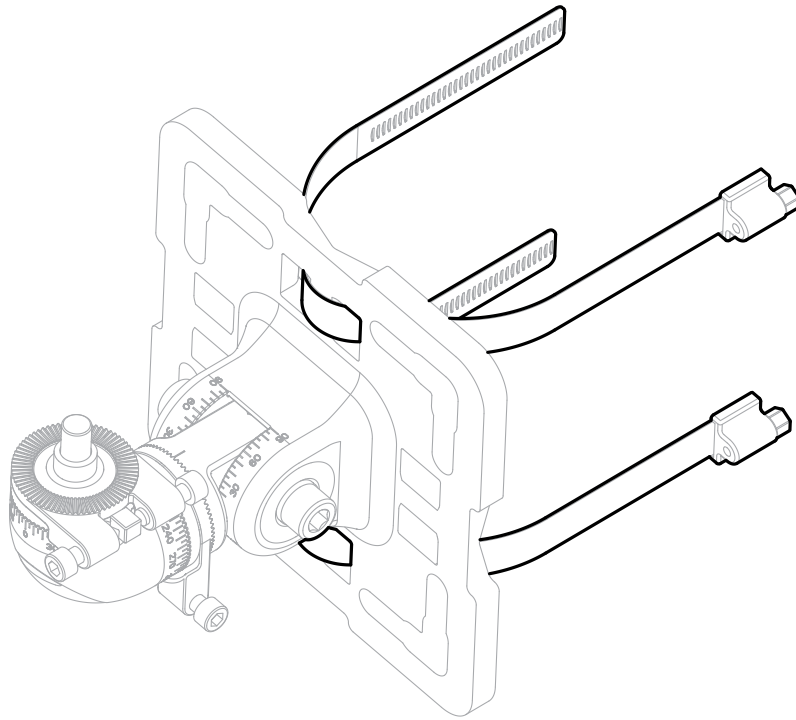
Montage der universellen Montagehalterung mit Schneckengewindeschellen
